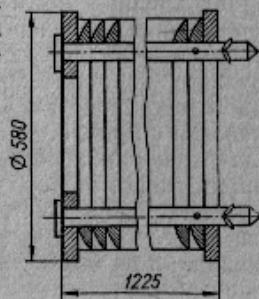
Общий вид грузового пакета колец на стержнях из отходов металла.
